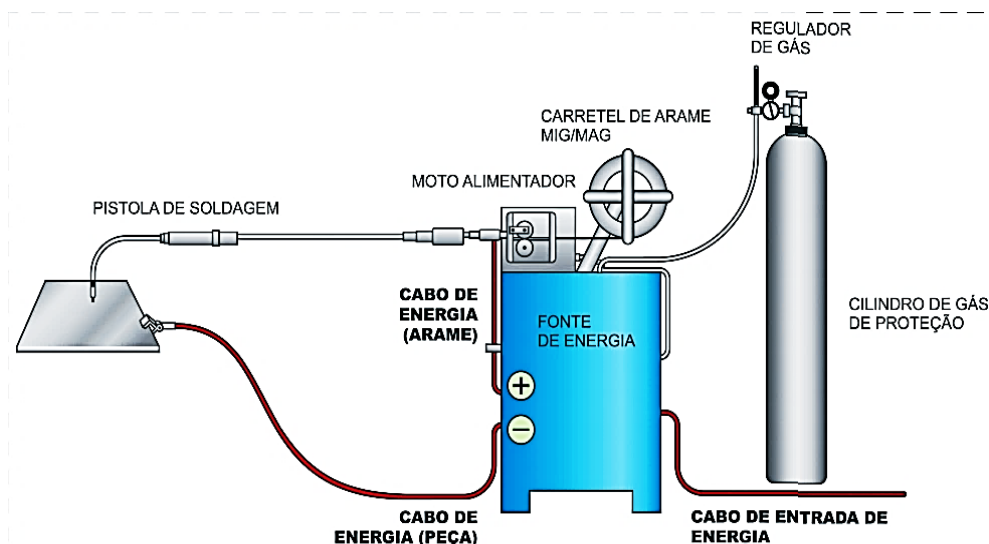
Esquema simples de componentes da soldagem MIG/MAG
